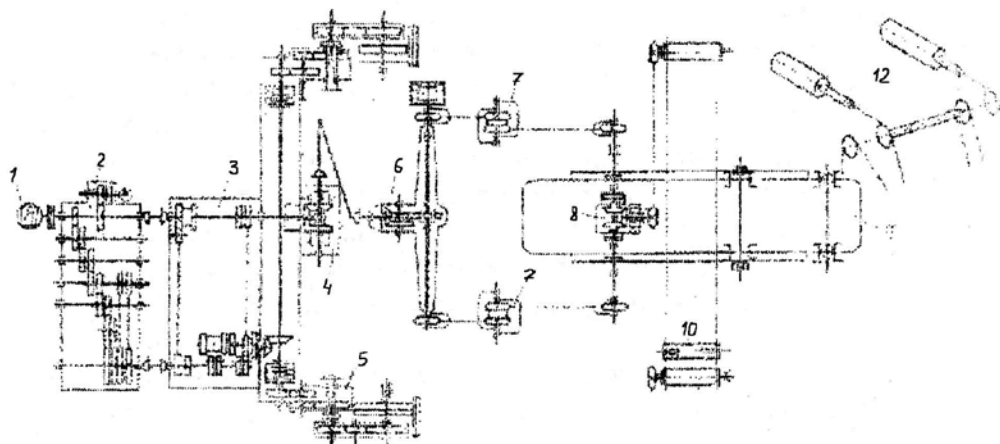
Кинематическая схема экскаватора ЭР-7АМ:
